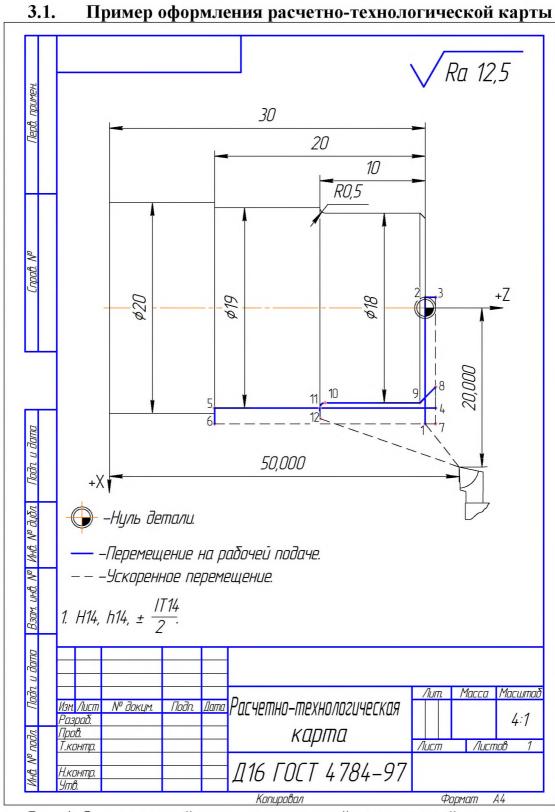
Операционный эскиз, совмещенный с траекторией движения инструмента
